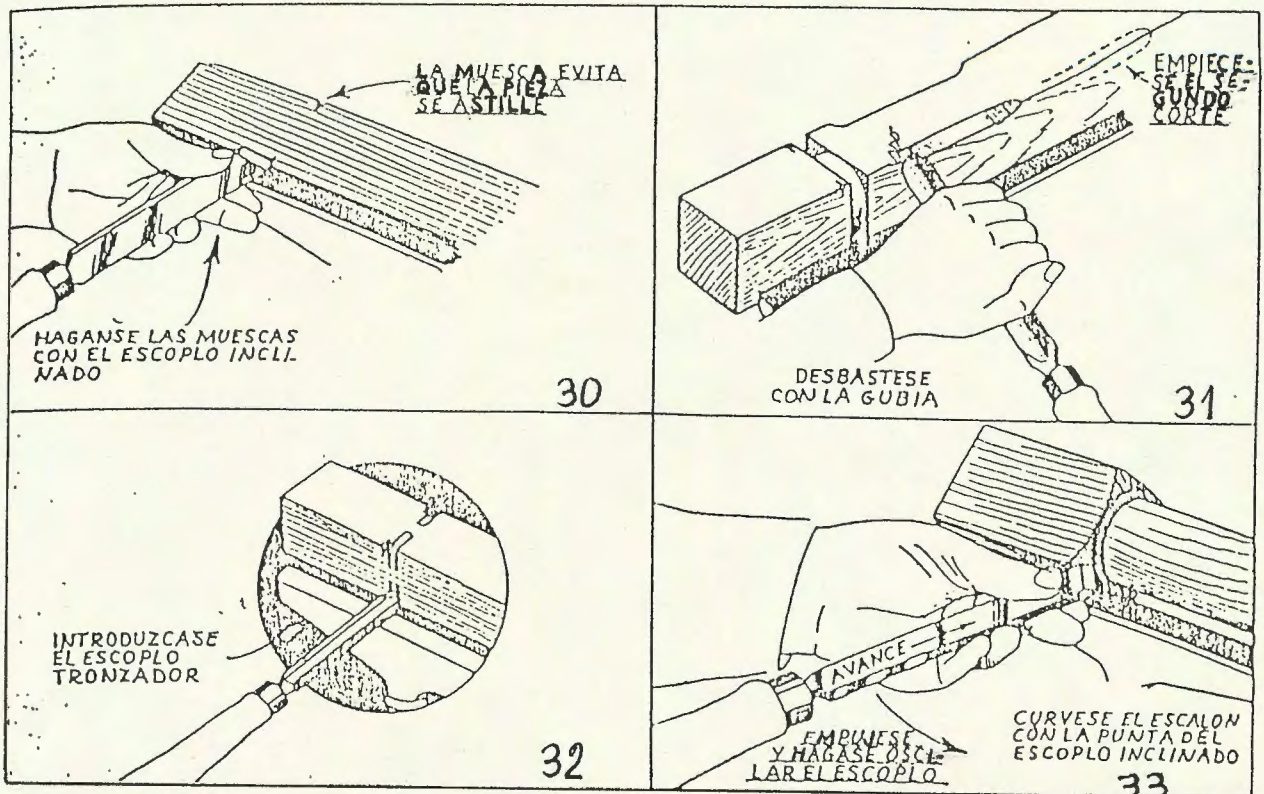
a 33.- Corte del Escalón del tramo cilíndrico al cuadrado.
